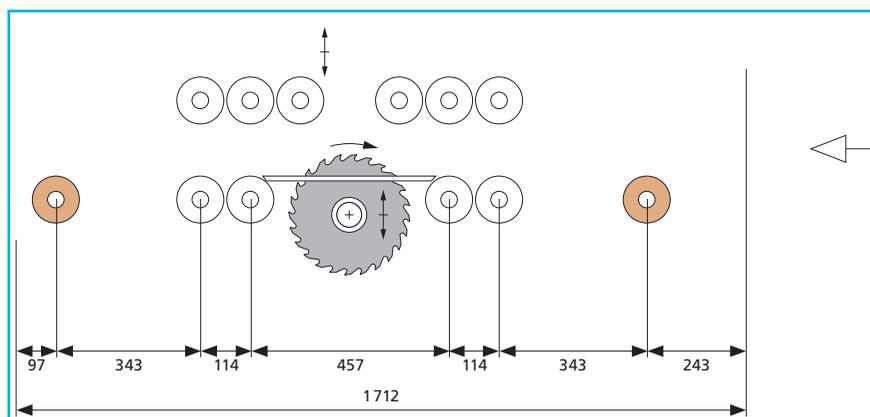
Walzenausstattung einer M34 mit Minimalausstattung
